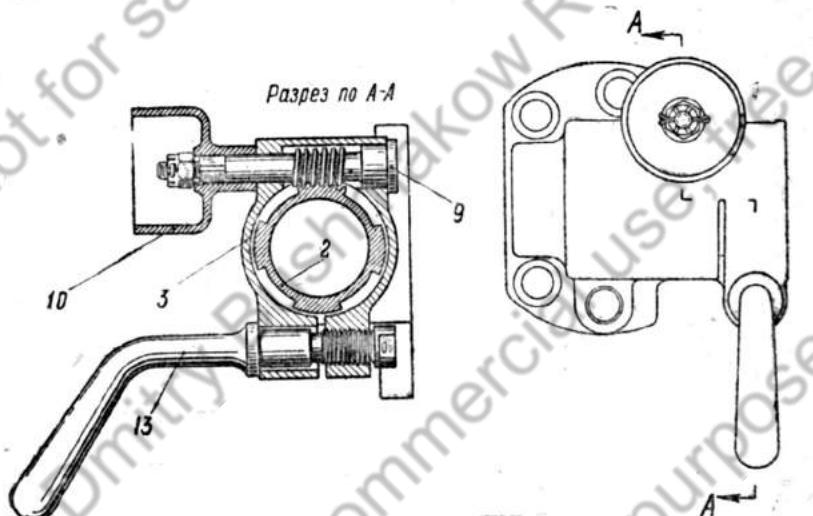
Собранный коробка крепления прицела (сб. 12):
